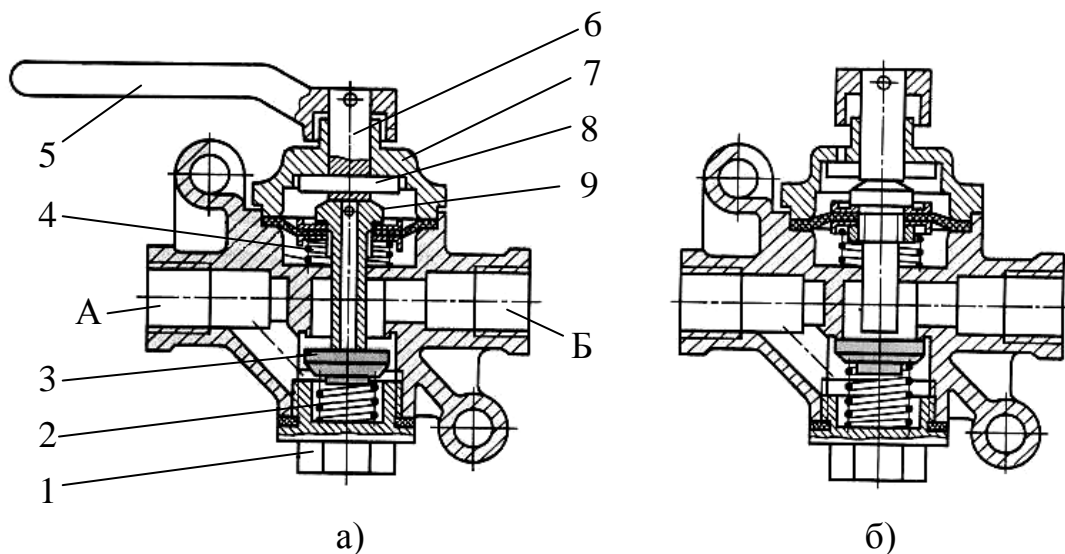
Конструкция разобщительного крана: а – кран открыт, б – кран закрыт; 1 – пробка; 2 и 4 – пружины; 3 – клапан; 5 – рукоятка; 6 – толкатель; 7 – крышка; 8 – штифт; 9 – шток с мембраной в сборе; А – вывод в пневмосистему тягача; Б – вывод к соединительной головке
